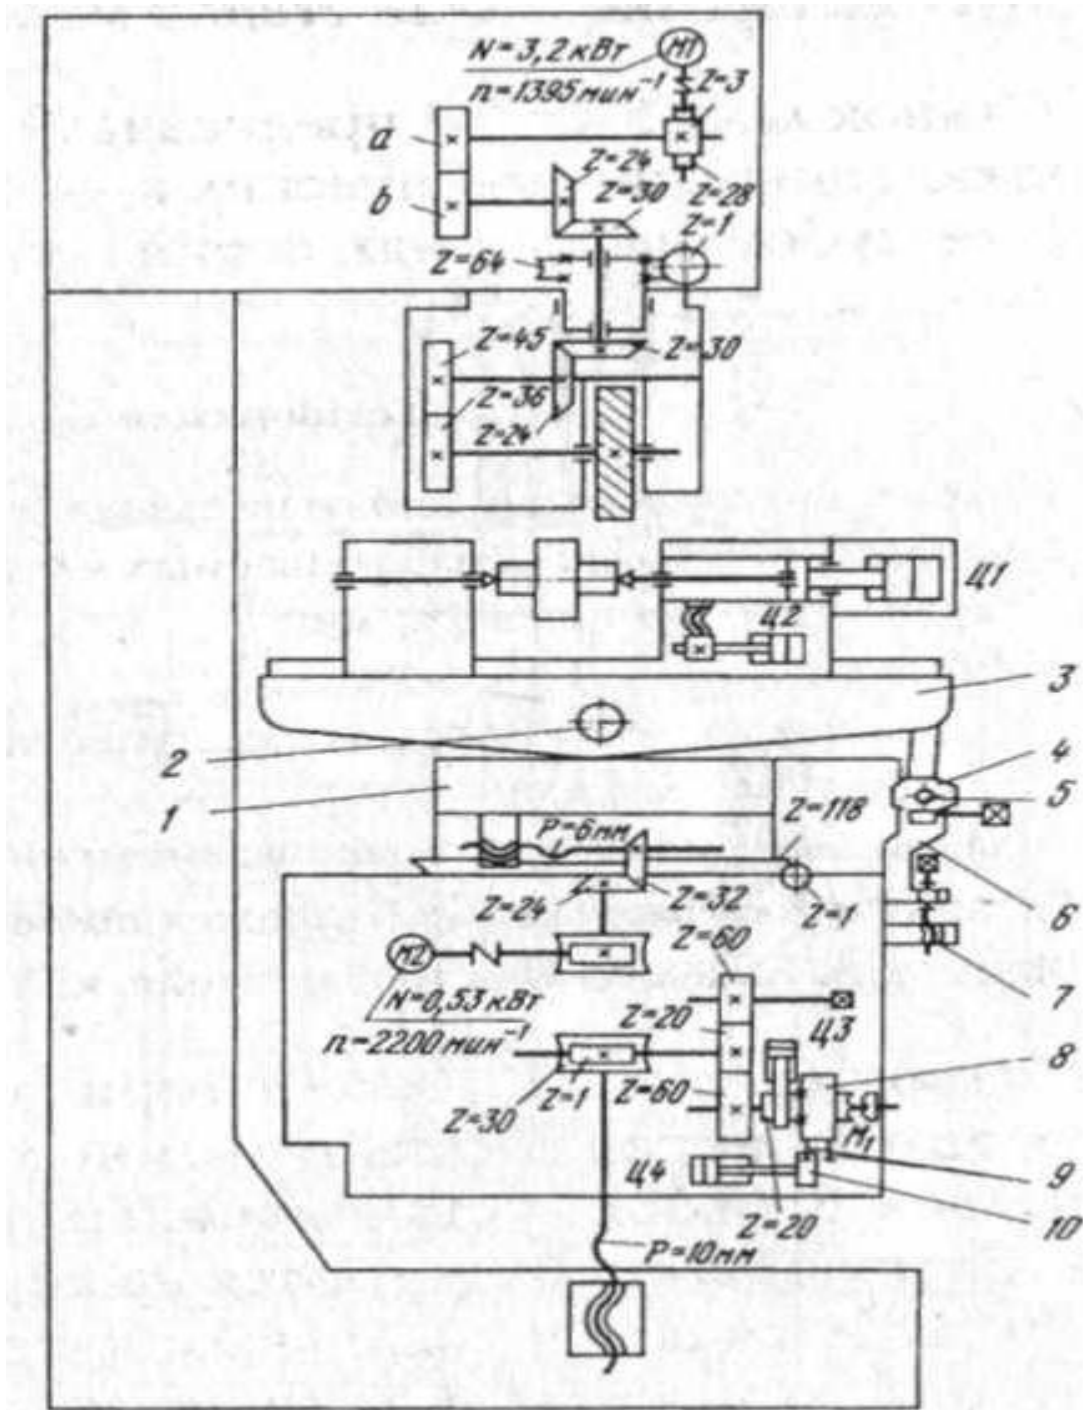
Кинематическая схема станка модели 5Б702В.
